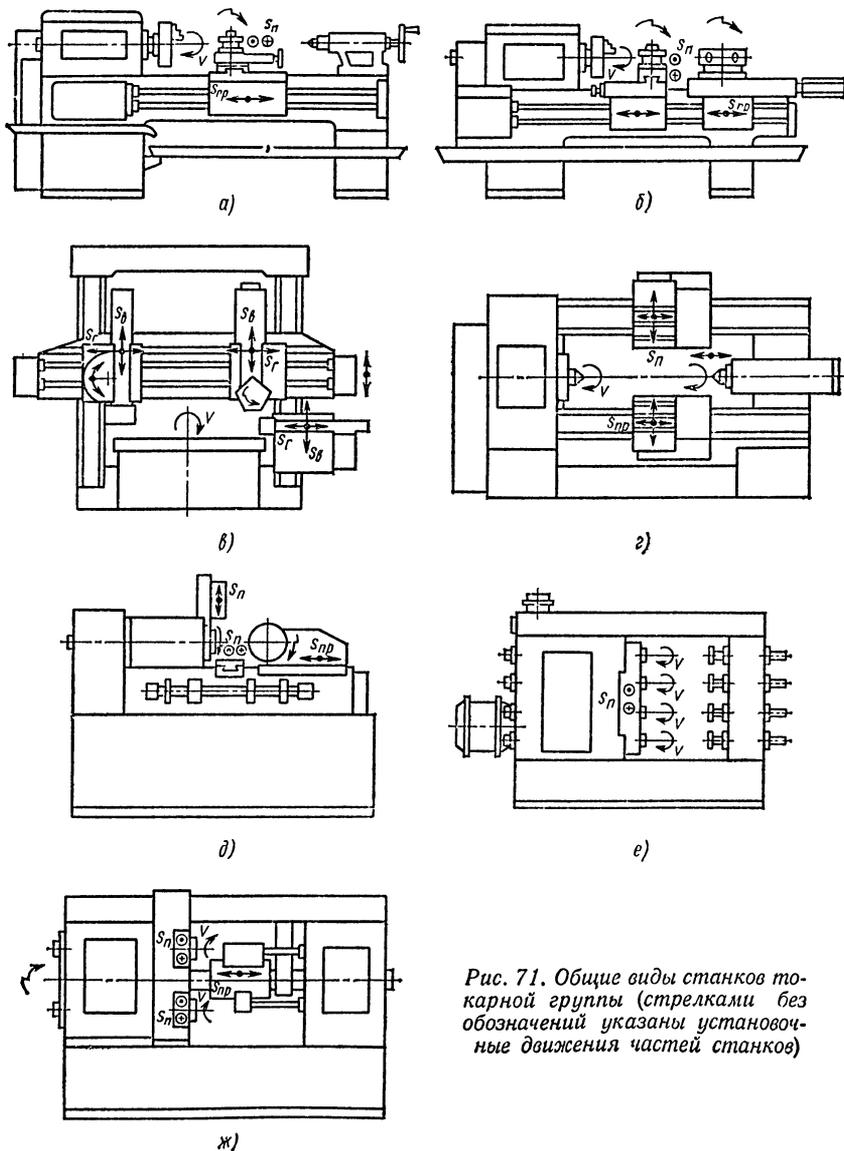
Общие виды станков токарной группы (стрелками без обозначений указаны установочные движения частей станков)
